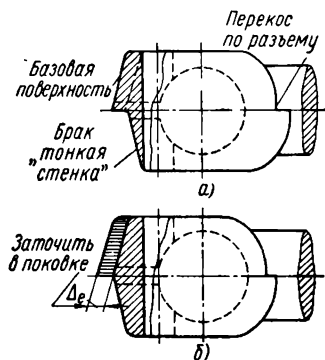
Исправление заточки незначительного перекоса в поковке на базовой поверхности: а — влияние перекоса на образование тонкой стенки; б — заточка и выравнивание базовой поверхности исправляет поковку и позволяет получить годную деталь
